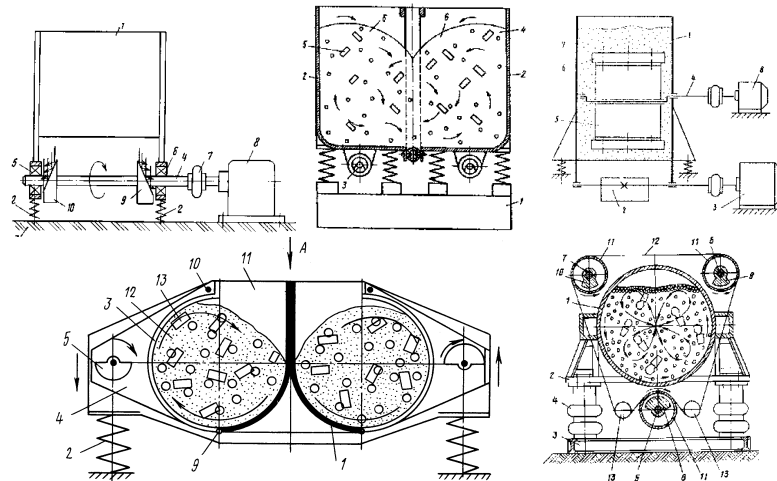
Схеми машин для вібраабразивної обробки деталей
